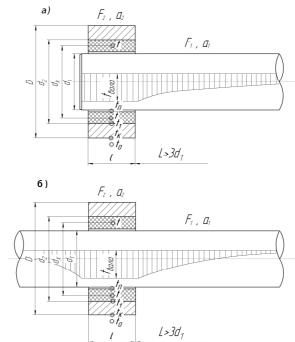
Схема подшипникового узла скольжения, когда вал вращается относительно неподвижной втулки: а — концевой подшипник; б — срединный подшипник: d_1 — диаметр вала в зоне трения; d_2 — наружный диаметр подшипника; D — наружный диаметр корпуса подшипника; l — длина подшипника; L_1, L_2 — длина вала с интенсивным теплообменом в левую и правую стороны от подшипника соответственно, t_i — температура в зоне трения, 0 С; t — температура в середине полимернометаллической втулки 0 С; t_1 — температура на внешней поверхности втулки, 0 С; t_k — температура на корпусе подшипника скольжения 0 С; t_0 — температура окружающей среды 0 С.
